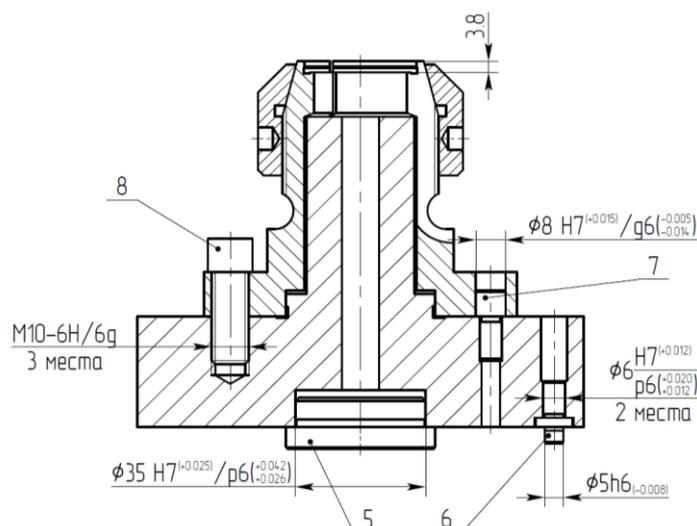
Станочное приспособление - Оправка зажимная для детали «Хомут»
